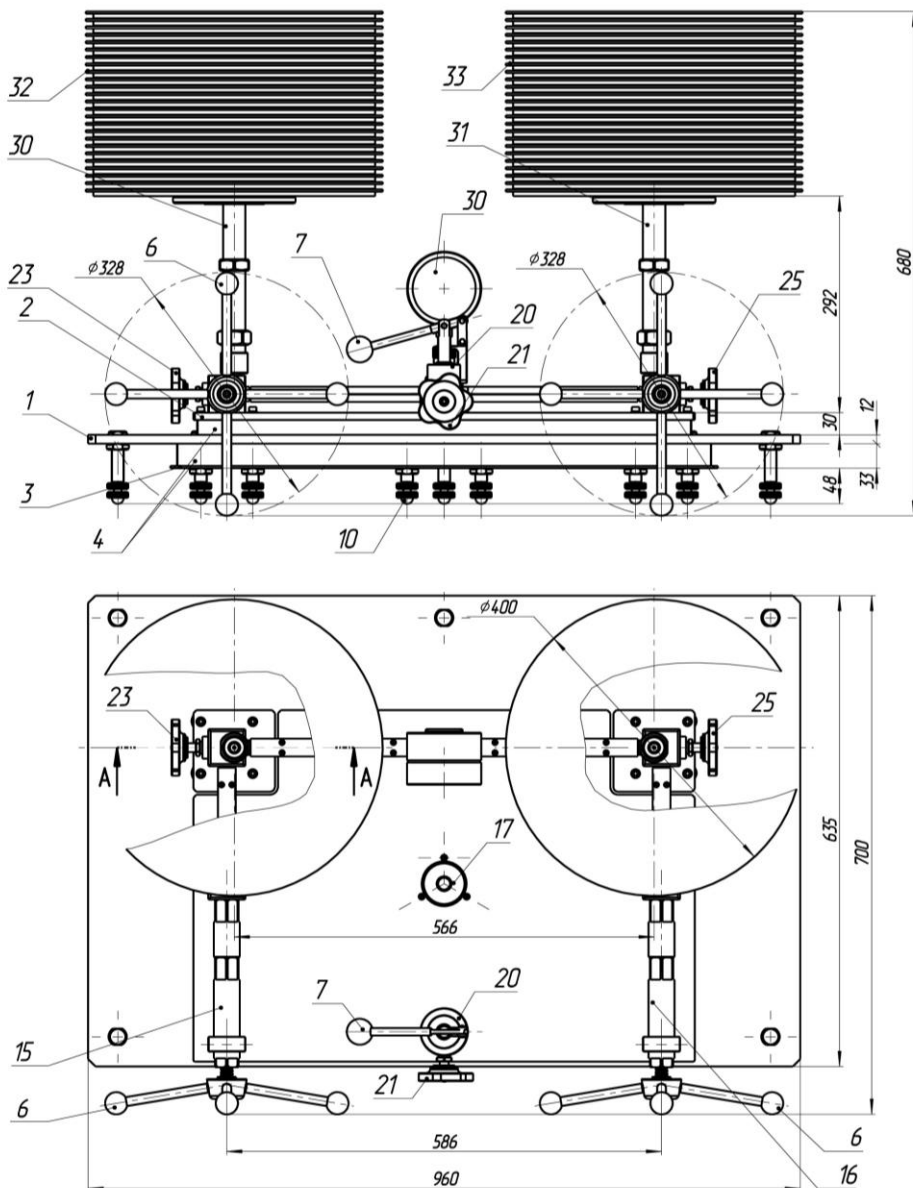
Внешний вид пресса гидравлического ПГ-2500
